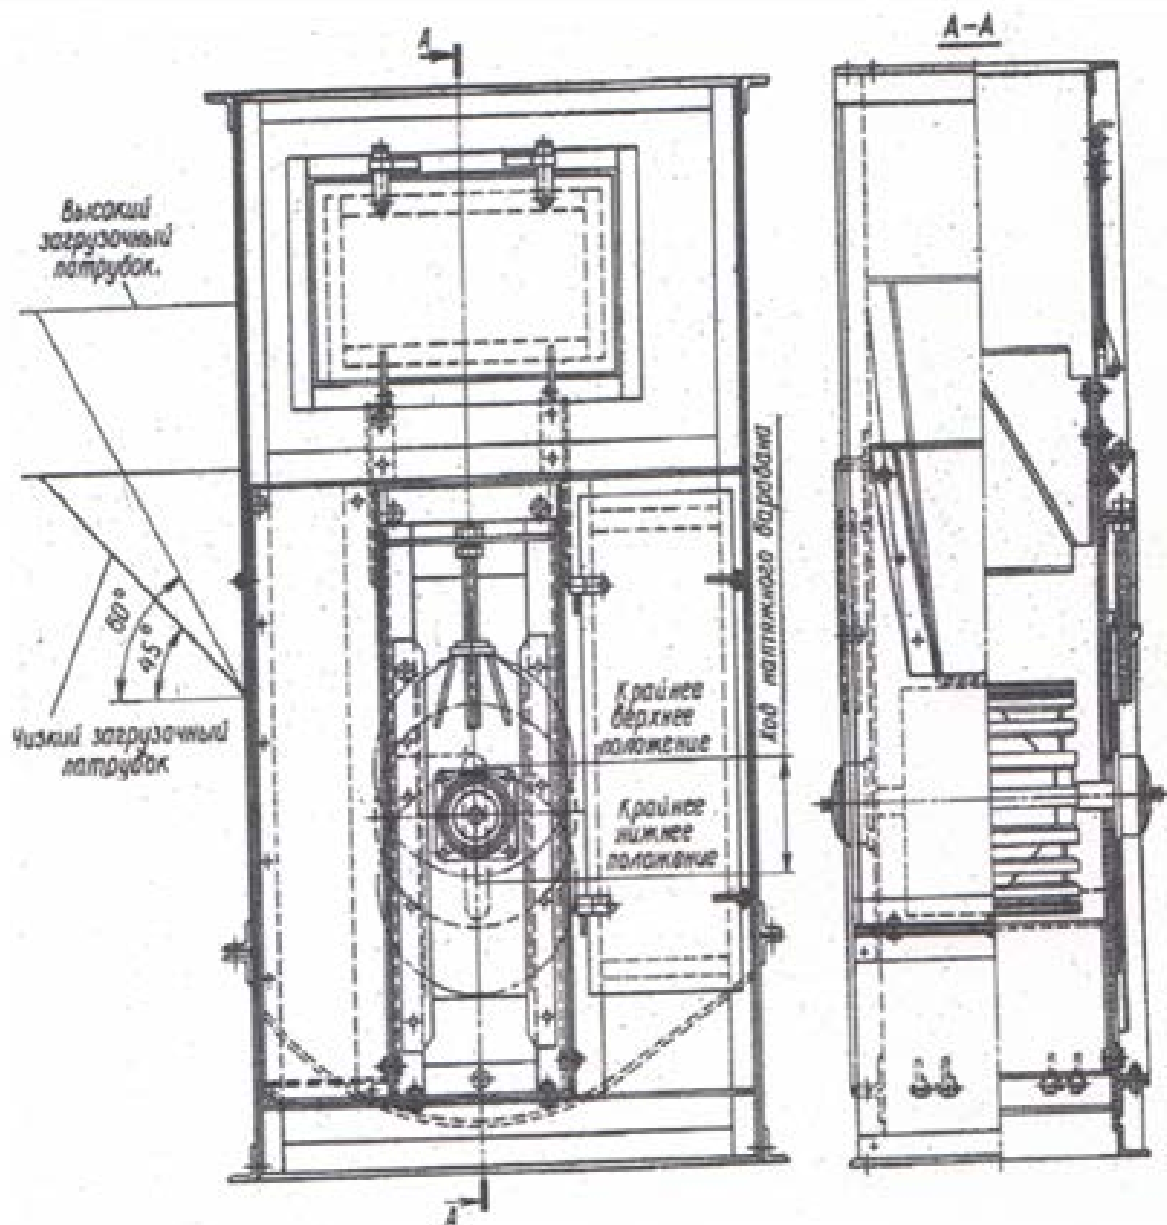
Нижняя часть кожуха и винтовое натяжное устройство вертикального ковшового ленточного элеватора
